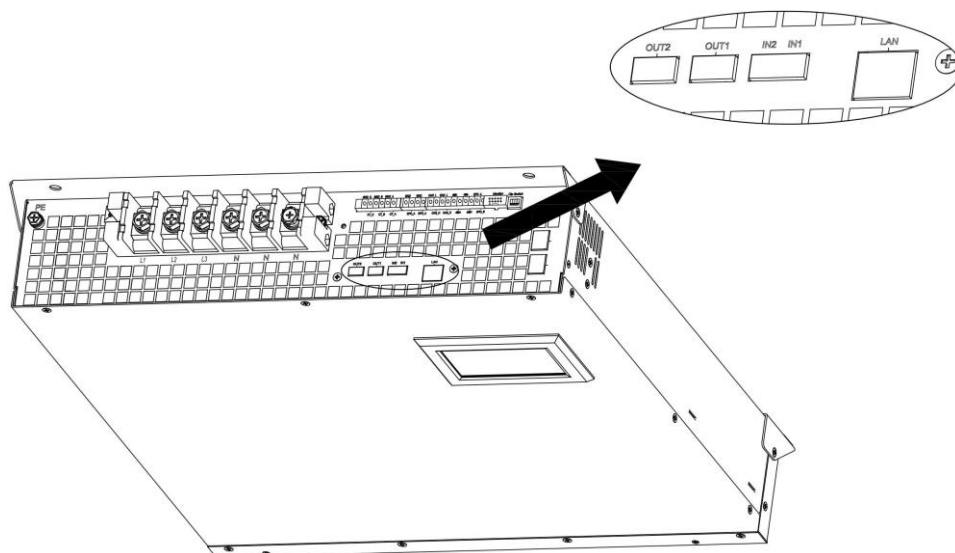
Posición del tablero de contactos Ultra dry AHF montado en la pared
